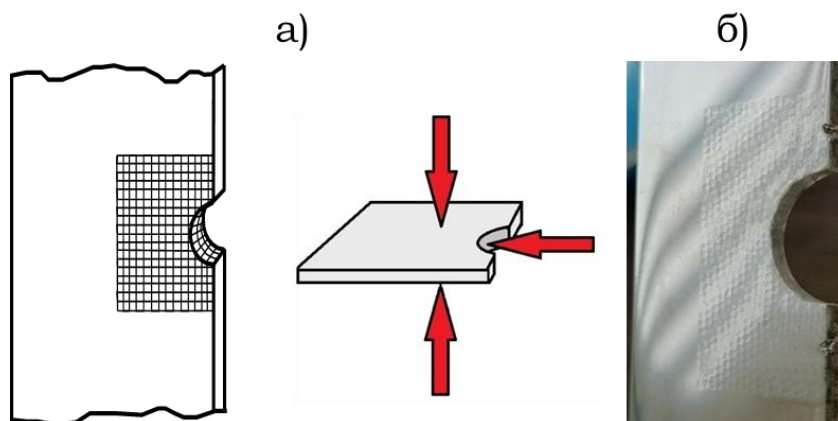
Схематичное изображение области и направления обработки (а) и фото обработанного образца (б)
